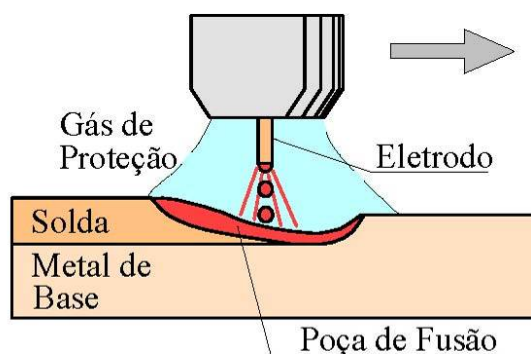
Processo de soldagem MIG/MAG (Modenesi e Marques, 2006).
